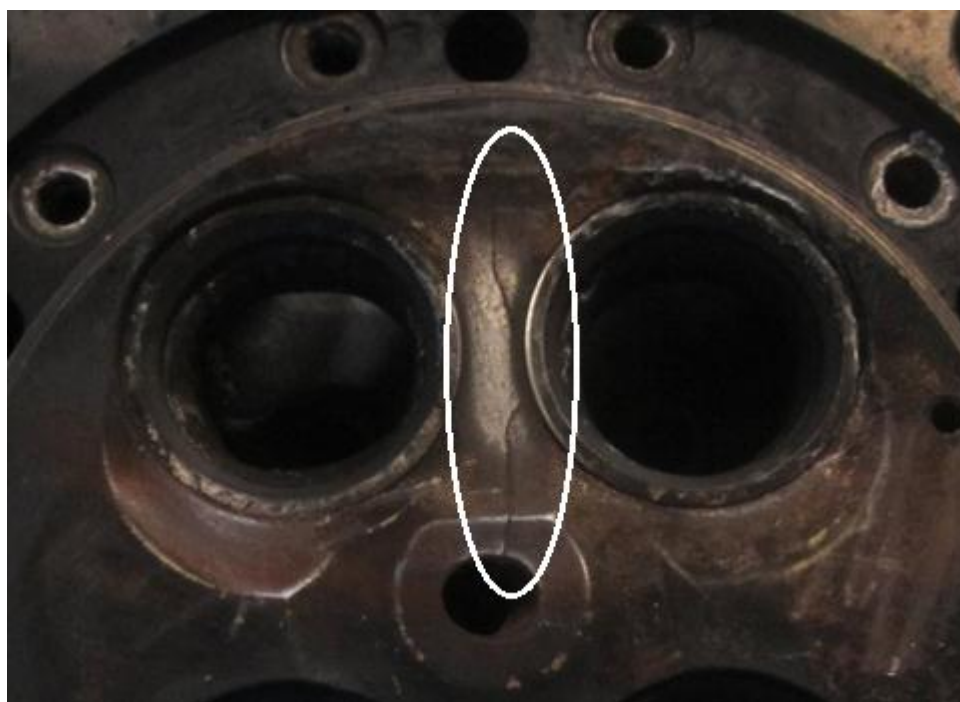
Продольная трещина межклапанной перемычки цилиндровой крышки дизельного двигателя горно-транспортной машины
